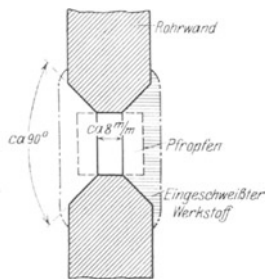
Verschweißen von Rohrwandlöchern.
